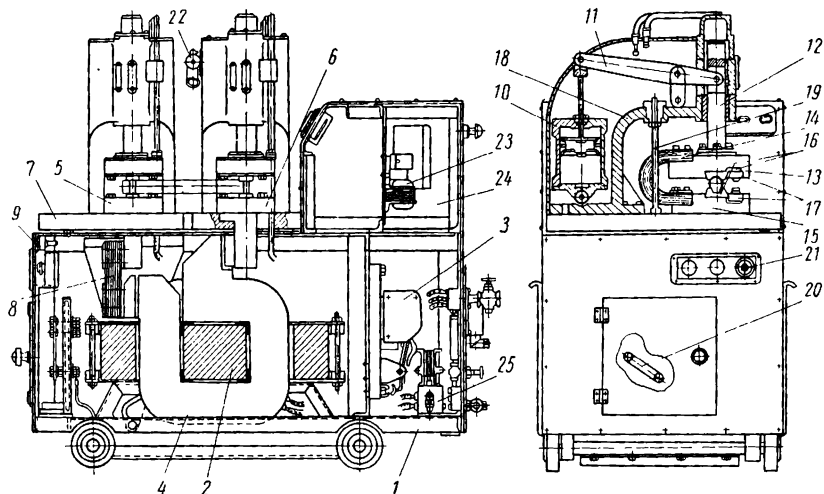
Типовая установка для нагрева методом сопротивления, типа К-16
